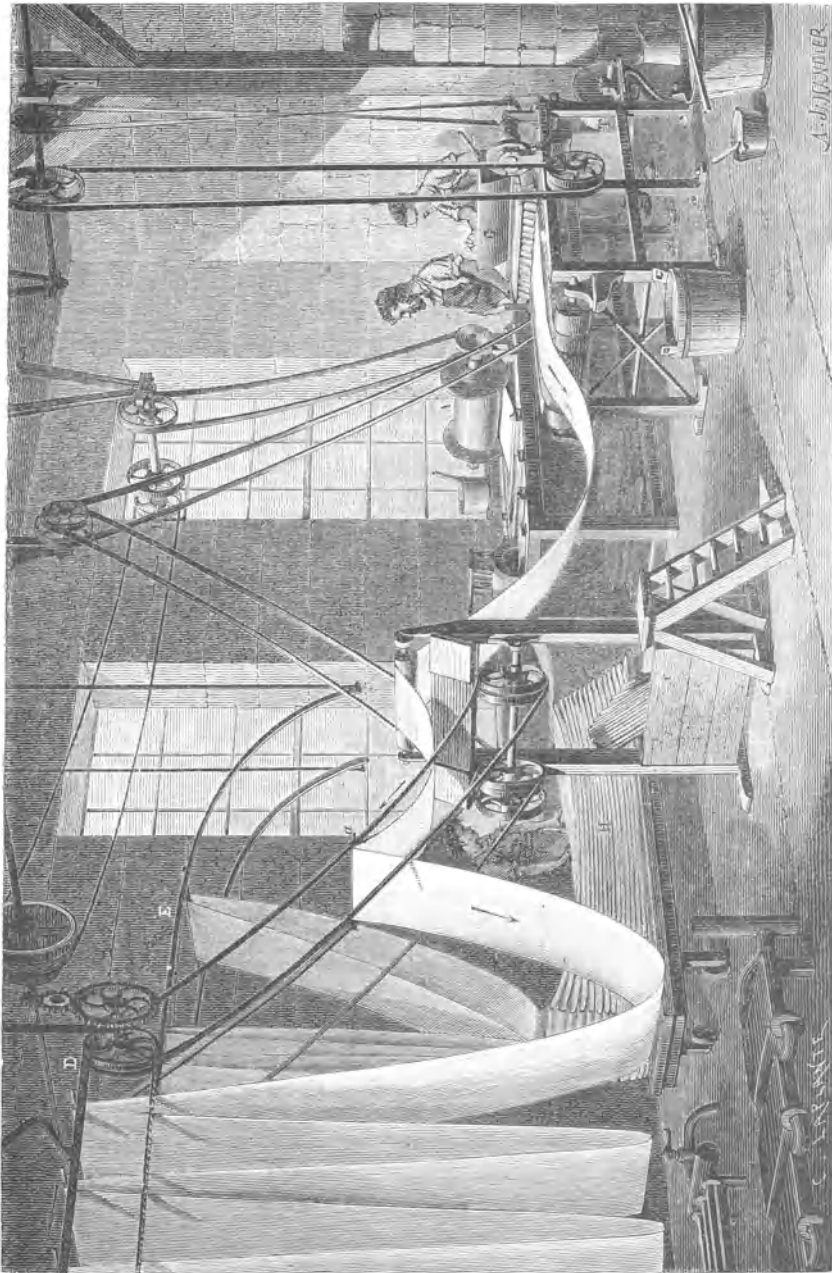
Grundriss der Papeten mittels Maschinen.
